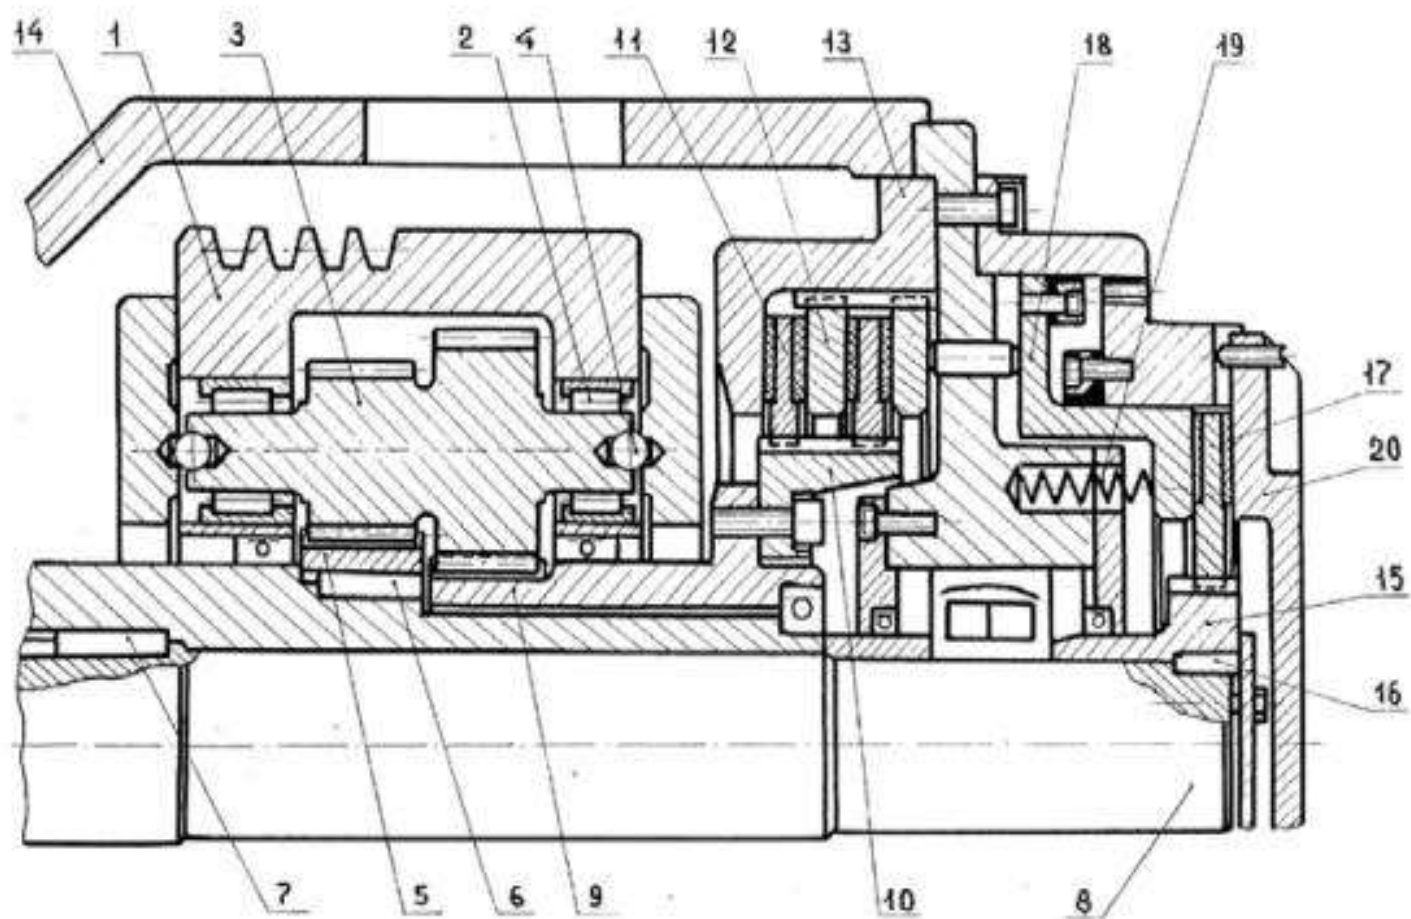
Схема привода с планетарным редуктором фирмы «Aida»
